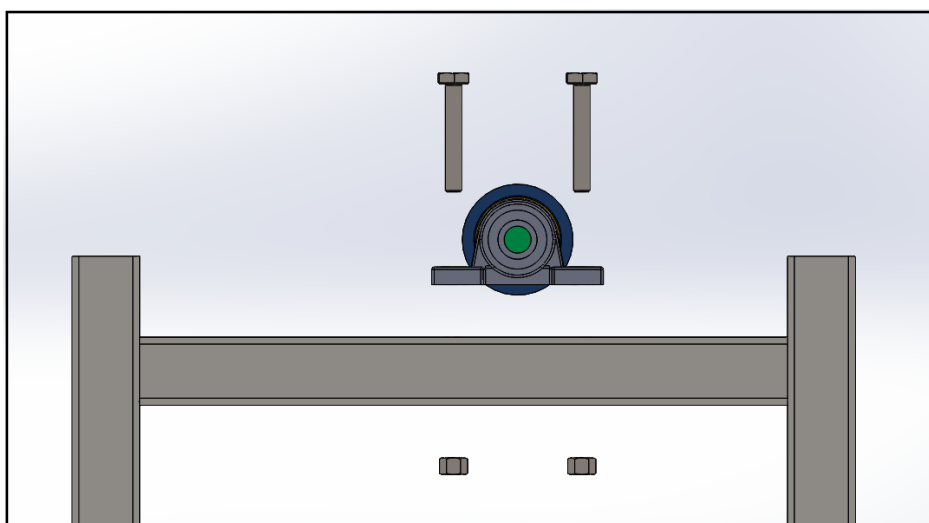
Συναρμολόγημα, POS20_CD_FRONT DRUM_SUB ASSEMBLY.
